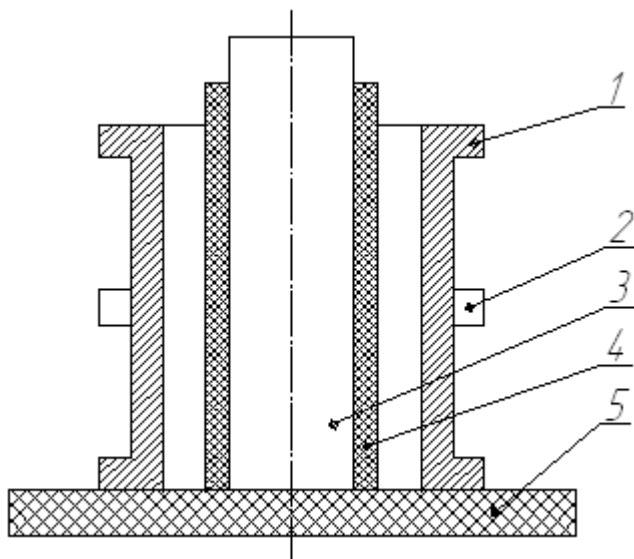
Схема сборки корпуса составного подшипника скольжения для заливки баббита
